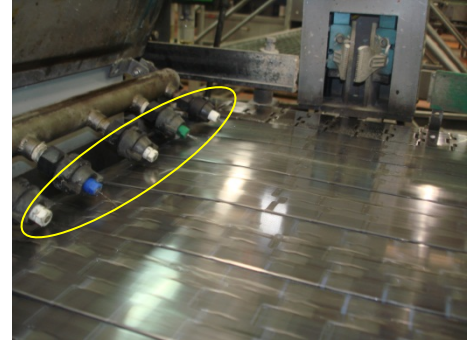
Verificar que las boquillas no tengan ninguna obstrucción.
